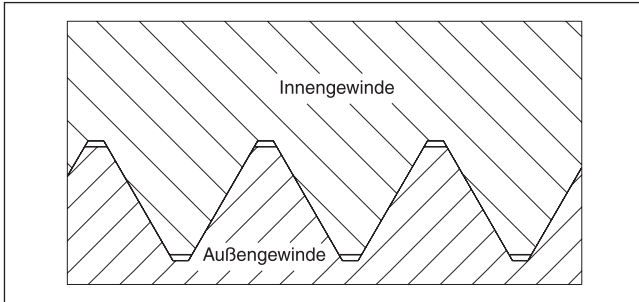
NPT – Schlüsselfest – Spiralförmiger Leckpfad bleibt, nur Flankenkontakt
